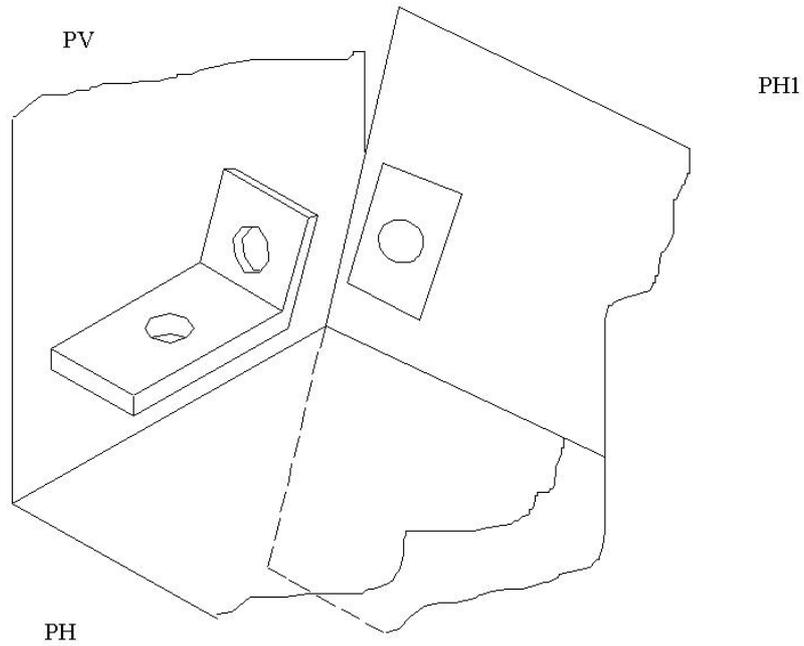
Realización de un cambio de plano Horizontal para obtener una vista auxiliar simple de la pieza.
